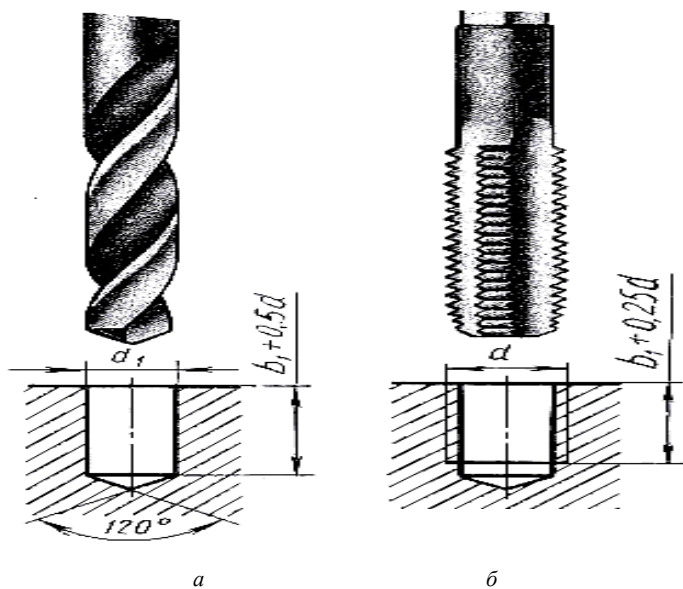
Последовательность изготовления внутренней резьбы: а – высверливание гладкого отверстия; б – нарезание резьбы метчиком
